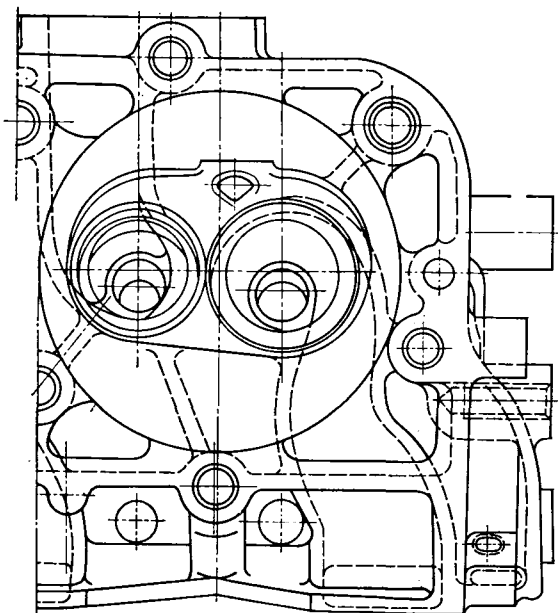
Конструкция головки блока с винтовыми впускными каналами
